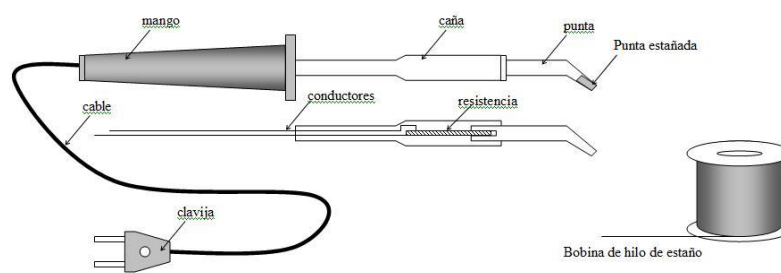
Equipo Usado para Realizar Soldadura Blanda
